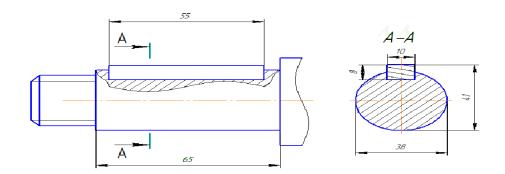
Шпоночное соединение ведущего шкива.
